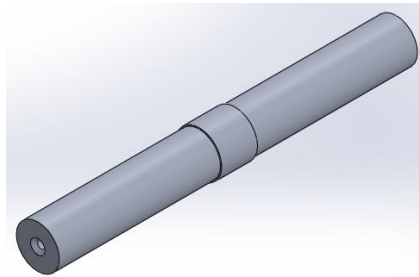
Modelagem do corpo de prova para o estudo de usinagem
